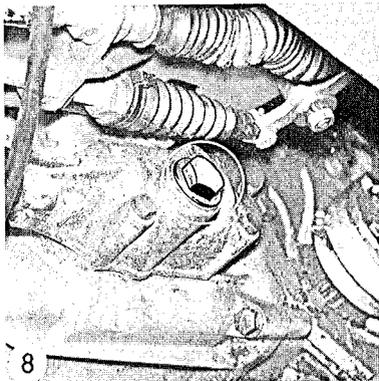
Getriebeöleinfüll- und Kontrollschraube
